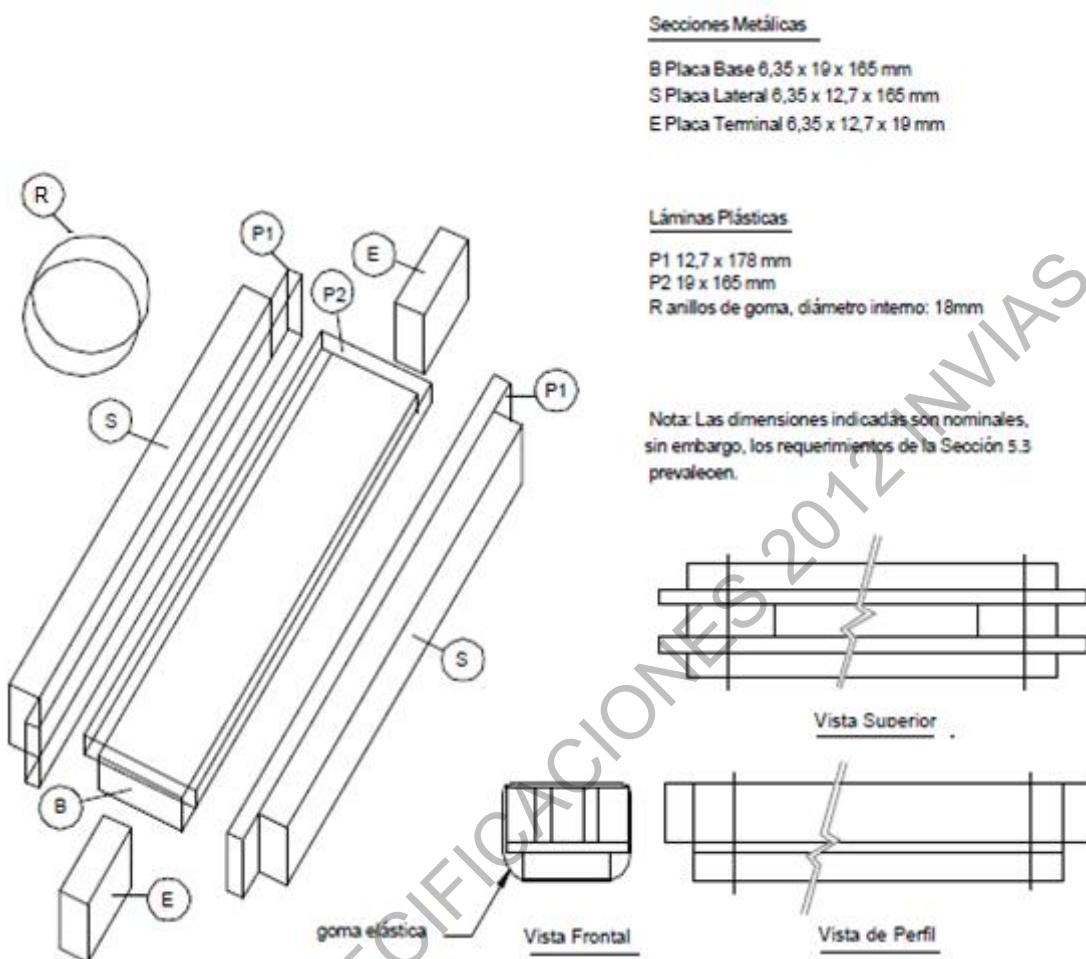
3. Dimensiones y especificaciones para los moldes de aluminio
